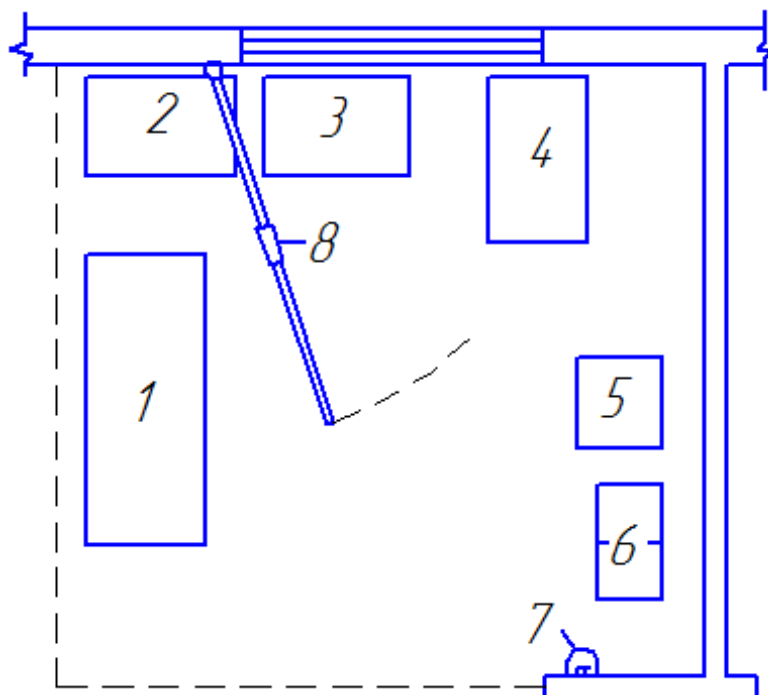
План дільниці з відновлення головок циліндрів: 1 - алмазно-розточний верстат; 2 - контрольний стіл; 3 – стенд для розбирання головок циліндрів; 4 - гідравлічний прес; 5 – тумбочка для інструменту; 6 – шафи для кодежі; 7 – раковина з водою; 8 – консольний кран.
